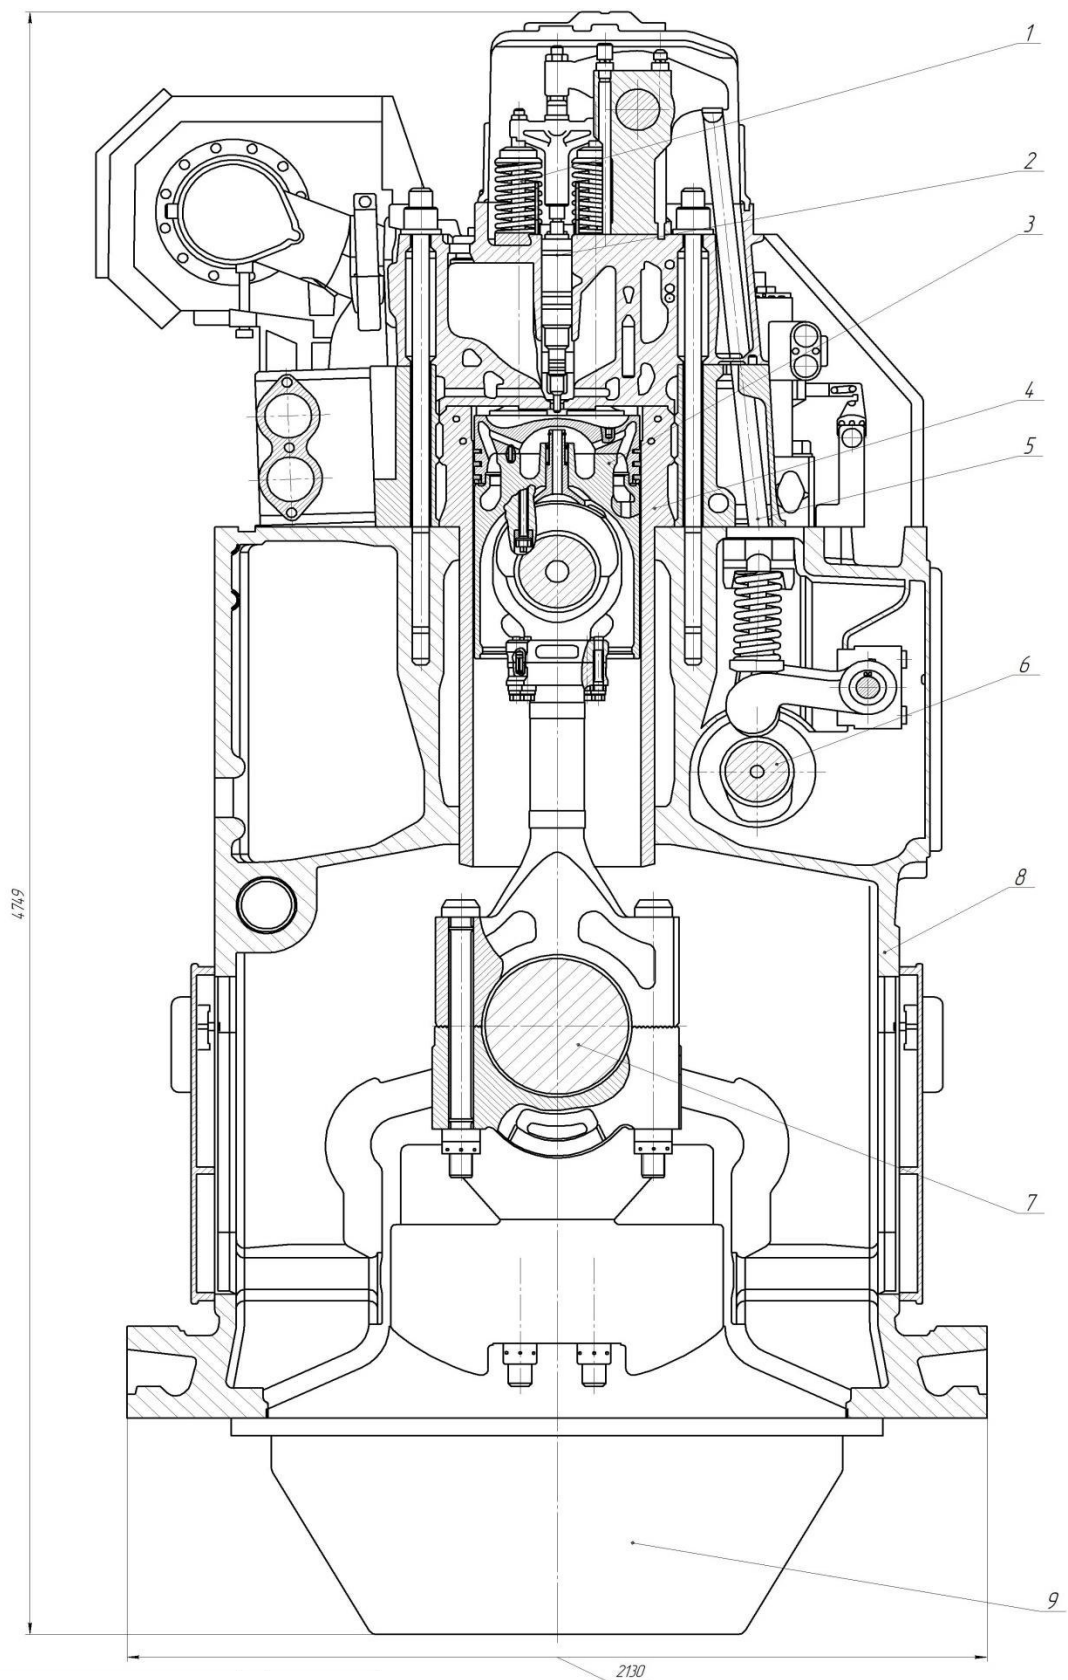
Поперечний переріз головного двигуна: 1 – клапан; 2 – паливна форсунка; 3 – поршень; 4 – циліндр; 5 – штовхач коромисла; 6 – шатун; 7 – колінчастий вал; 8 – блок-картер; 9 – піддон картера
